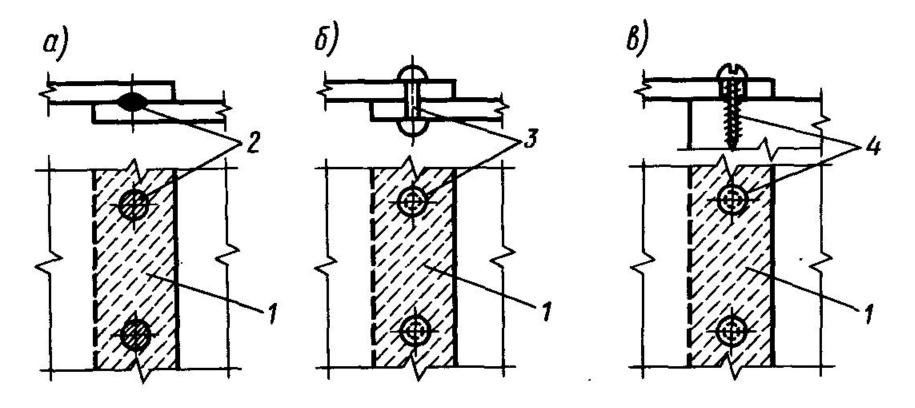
Клееметаллические соединения алюминиевых листов:
